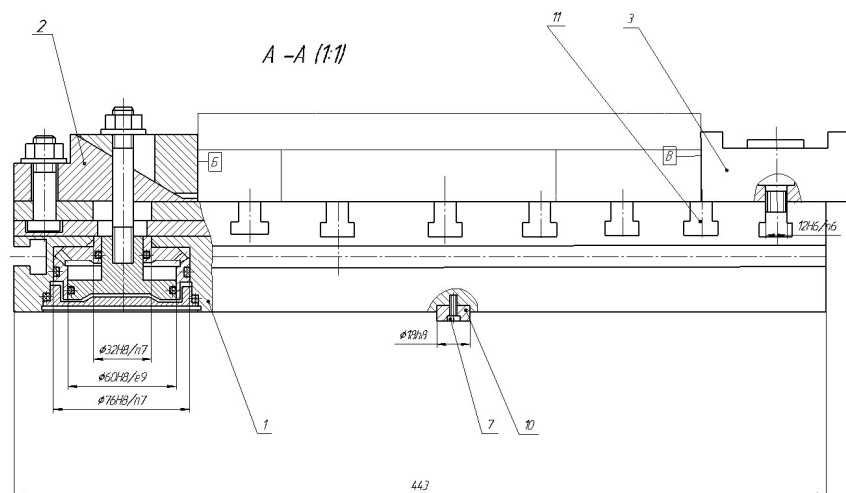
Загальний вигляд пристрою для фрезерування
